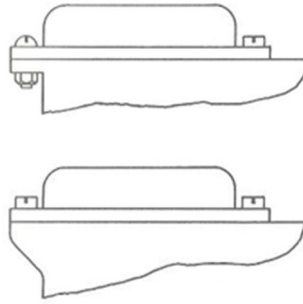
Conjunto de difícil montagem e alternativa [adaptado de [7]]
